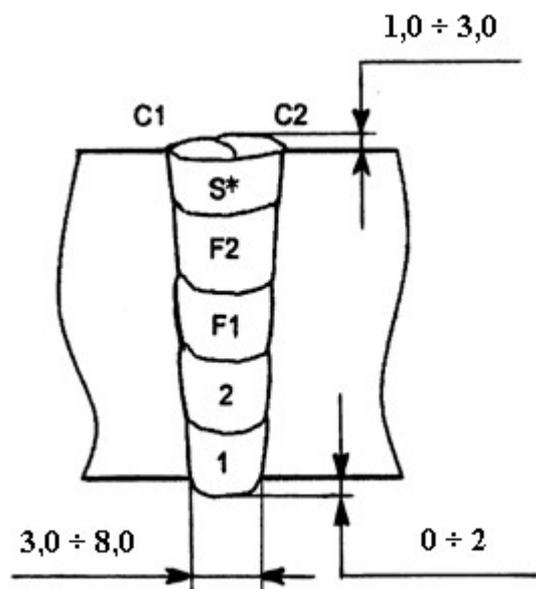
Схема и последовательность автоматической сварки кольцевого стыка
